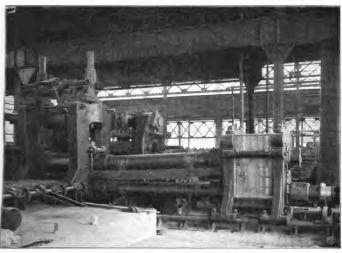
Blechwalzwerksanlage der Bethlehem Steel Co., Bethlehem, Pa.
